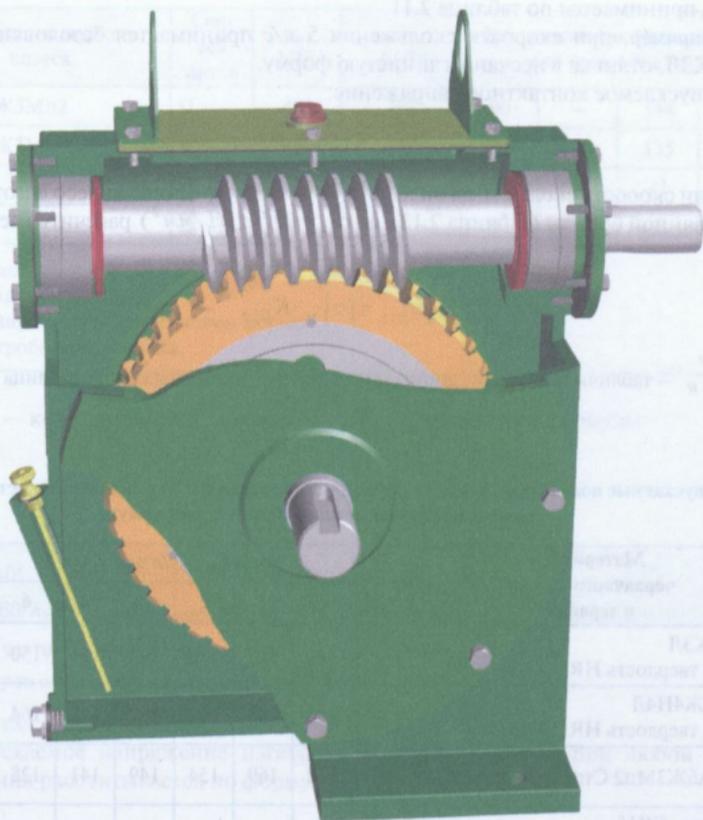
Редуктор червячный одноступенчатый с верхним расположением червяка
